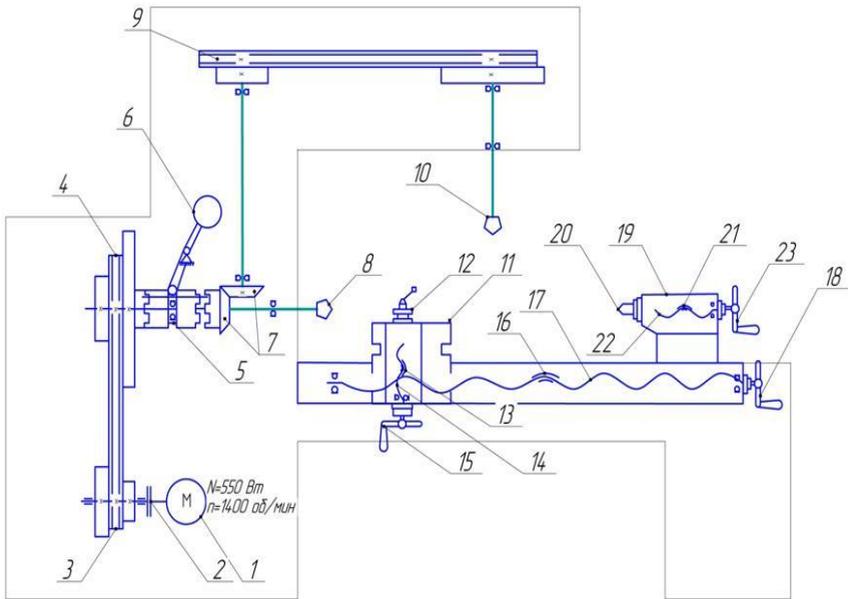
Кинематическая схема токарно-сверлильного станка мод. HQ-400: 1 – электродвигатель; 2 – муфта компенсирующая; 3 – ведущий шкив ремённой передачи; 4 – ведомый шкив ремённой передачи; 5 – муфта кулачковая; 6 – рукоятка переключения кулачковой муфты; 7 – ведущая шестерня конической передачи; 8 – шпиндель токарный; 9 – ремённая передача; 10 – шпиндель сверлильной головки; 11 – суппорт; 12 – резцедержатель; 13 – гайка винта поперечной подачи; 14 – винт поперечной подачи; 15 – маховик винта поперечной подачи; 16 – гайка винта продольной подачи; 17 – винта продольной подачи; 18 – маховик винта продольной подачи; 19 – задняя бабка; 20 – центр задней бабки; 21 – гайка винта осевой подачи; 22 – винт осевой подачи; 23 – маховик винта осевой подачи
